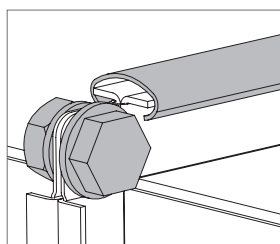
Collegamento del ventilatore tramite bulloni e profilo a C
